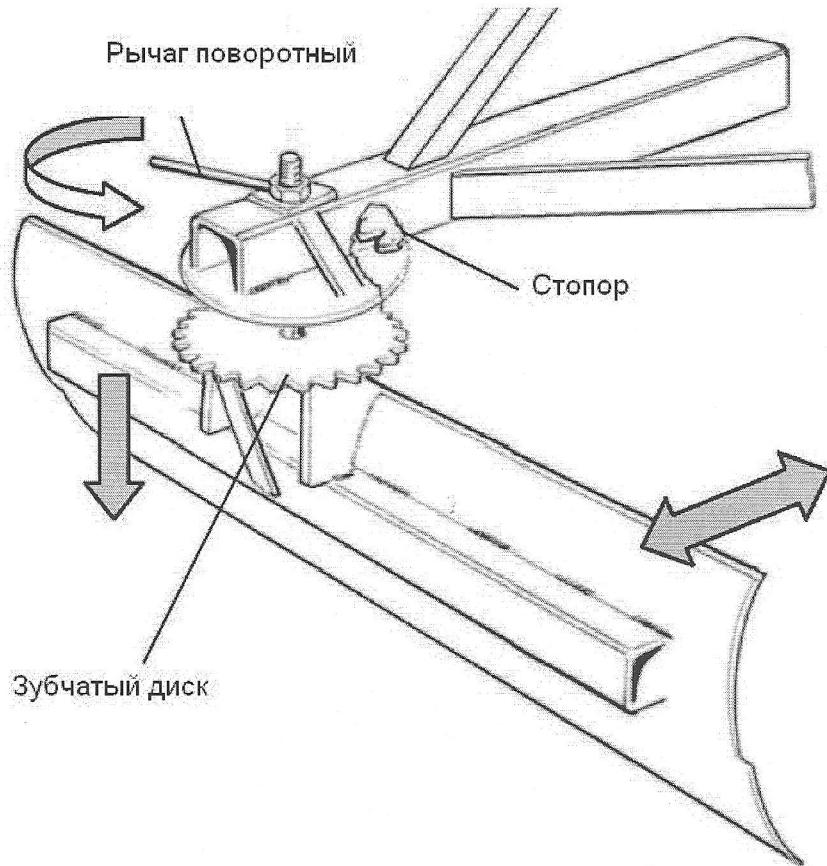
Регулировка угла атаки ножа лопаты с помощью поворотного кронштейна
